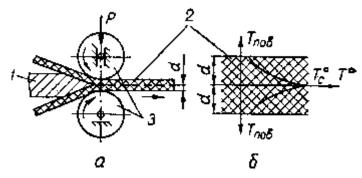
Непрерывная сварка пленок внахлестку:
